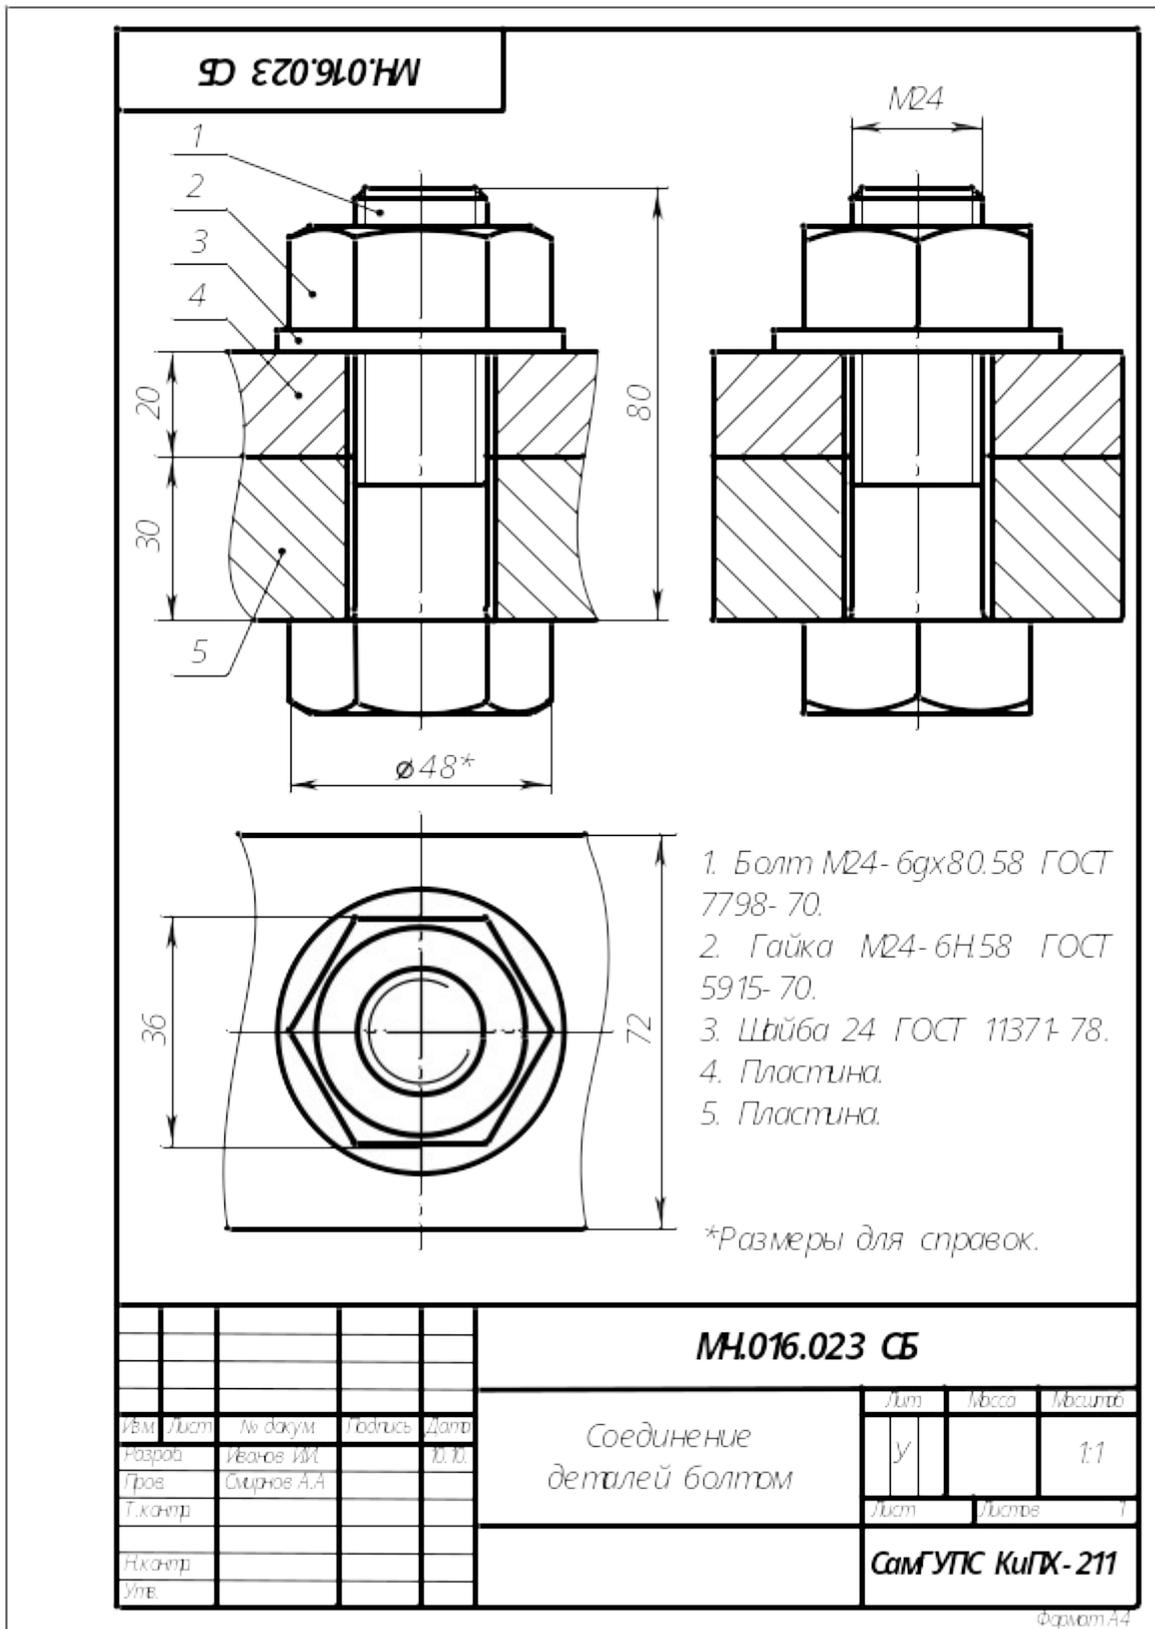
Образец выполнения чертежа «Соединение деталей болтом»
